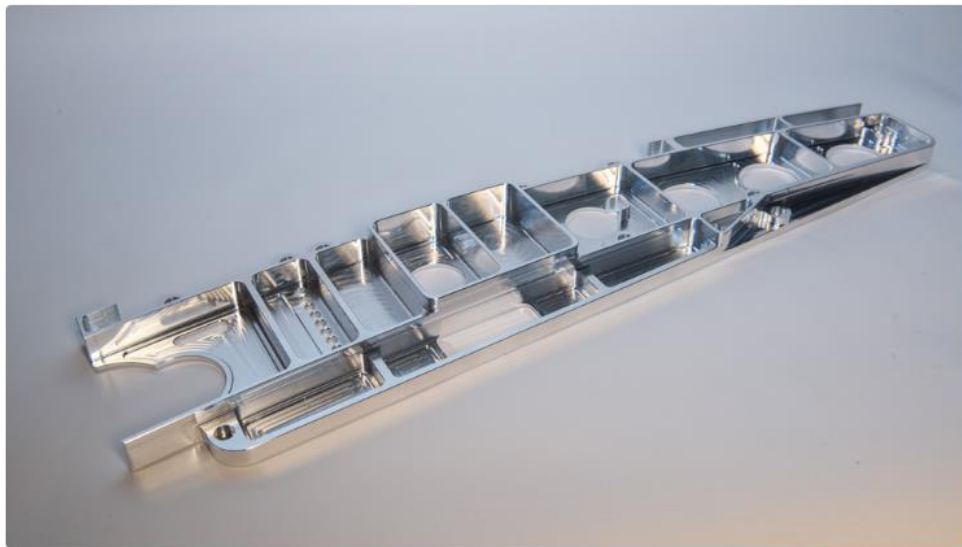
Элемент аэродинамического профиля самолета после фрезерной обработки на станке с ЧПУ
